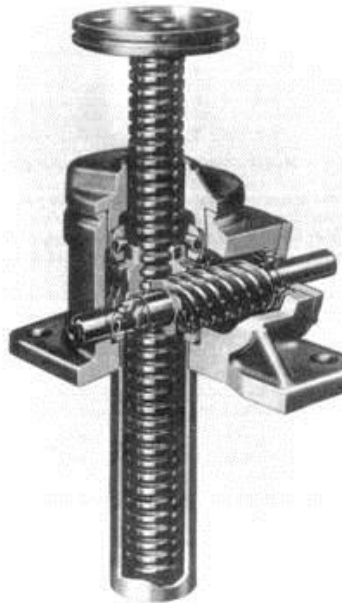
Mecanismo de sinfín de un levantador mecánico Joyce.
